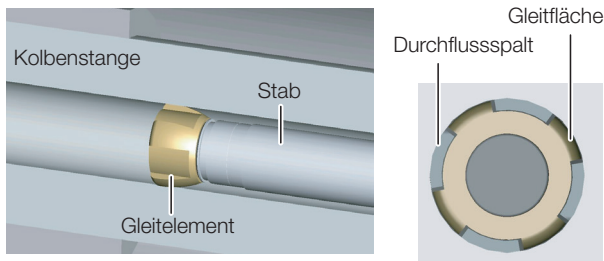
Detailansicht und Draufsicht Gleitelement
